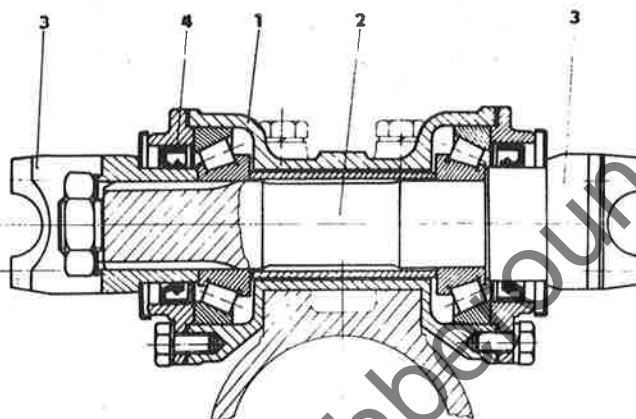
Kloubový hřídel přední nápravy a přední kloubový
